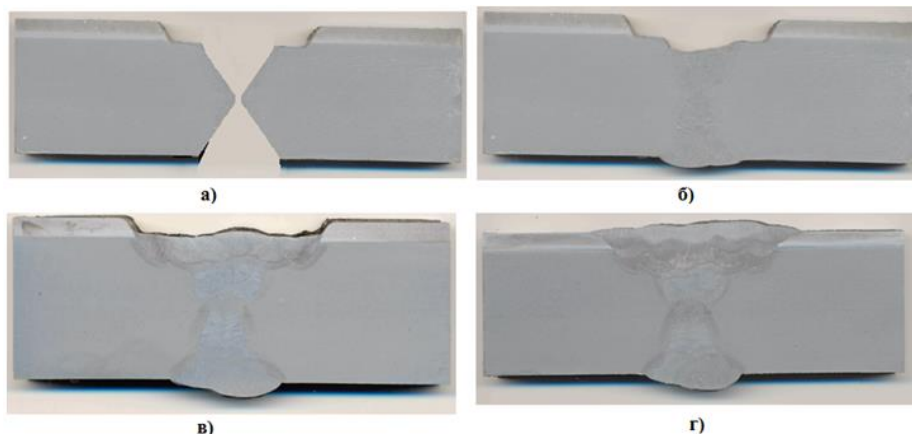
Основные этапы получения сварного соединения плакированной стали [3]:
